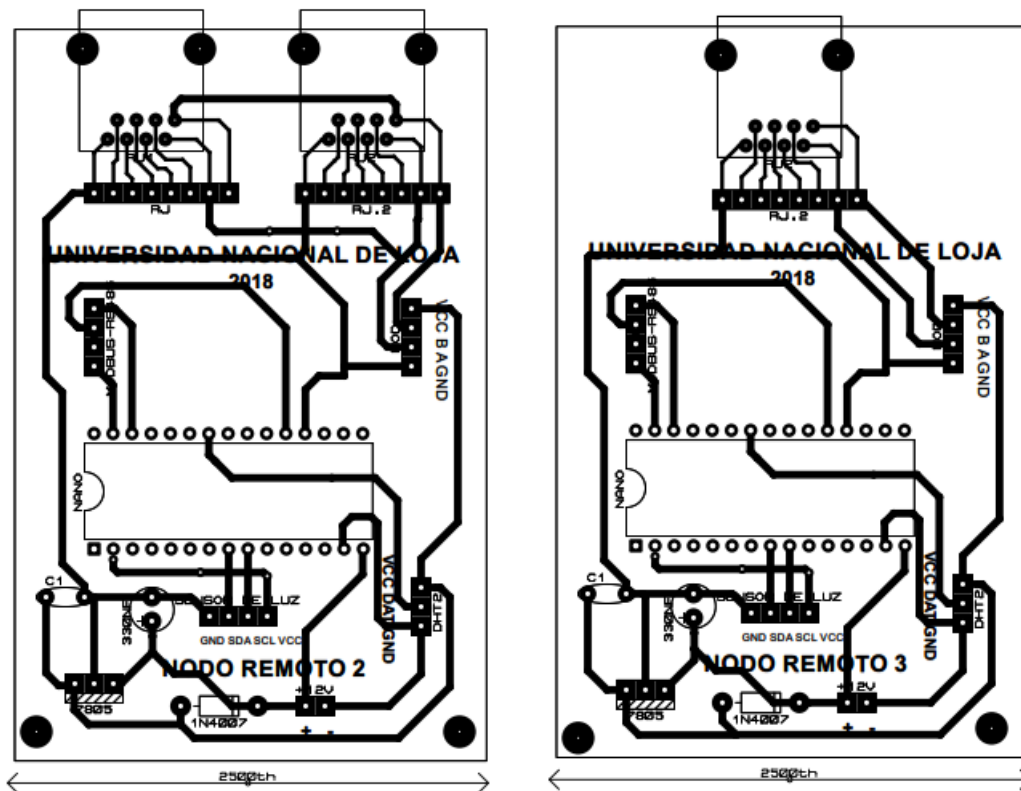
Diseño de circuito para PCB Nodo Remoto 2 y Nodo Remoto 3. Fuente [El Autor]
